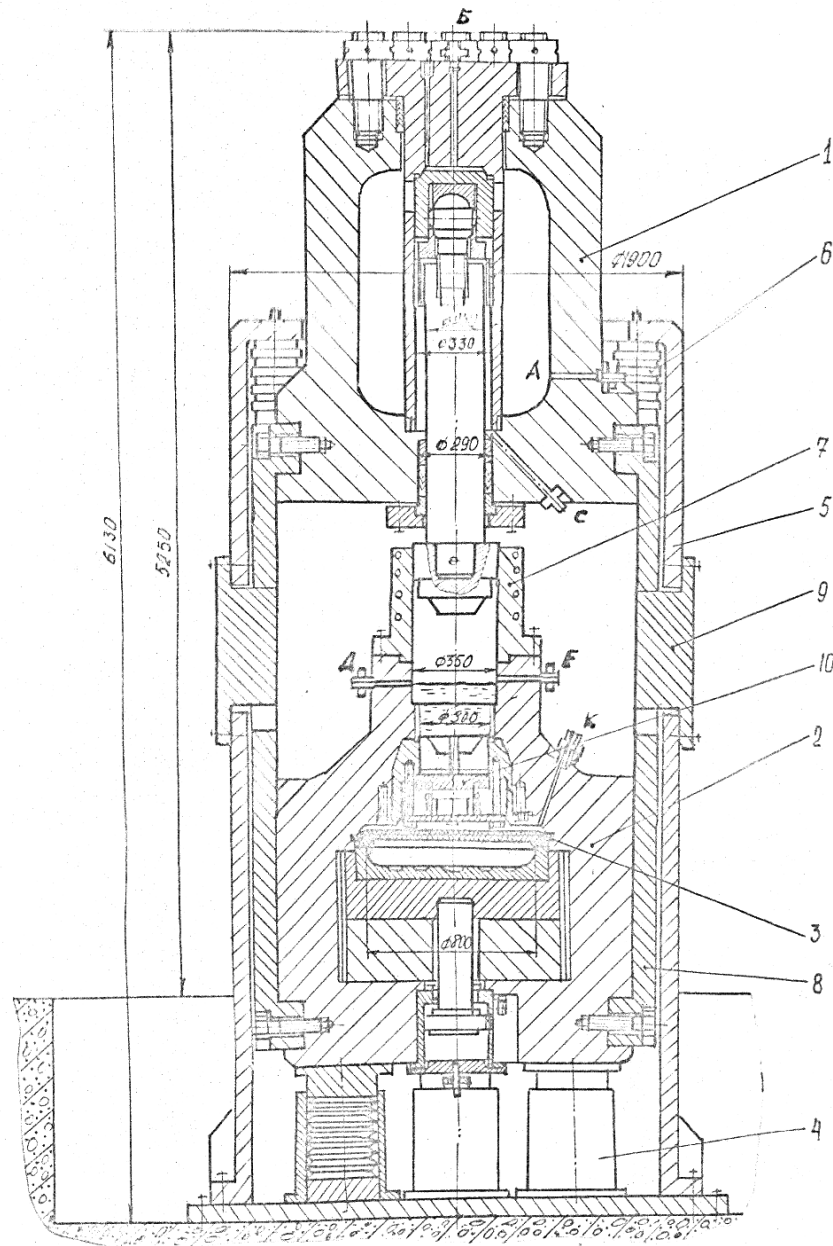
Установка для статико-динамічного листового штампування
